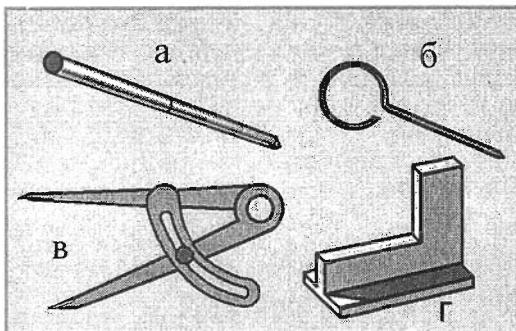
Разметочный инструмент: а – кернер; б – чертилка; в – слесарный циркуль; г – слесарный угольник
